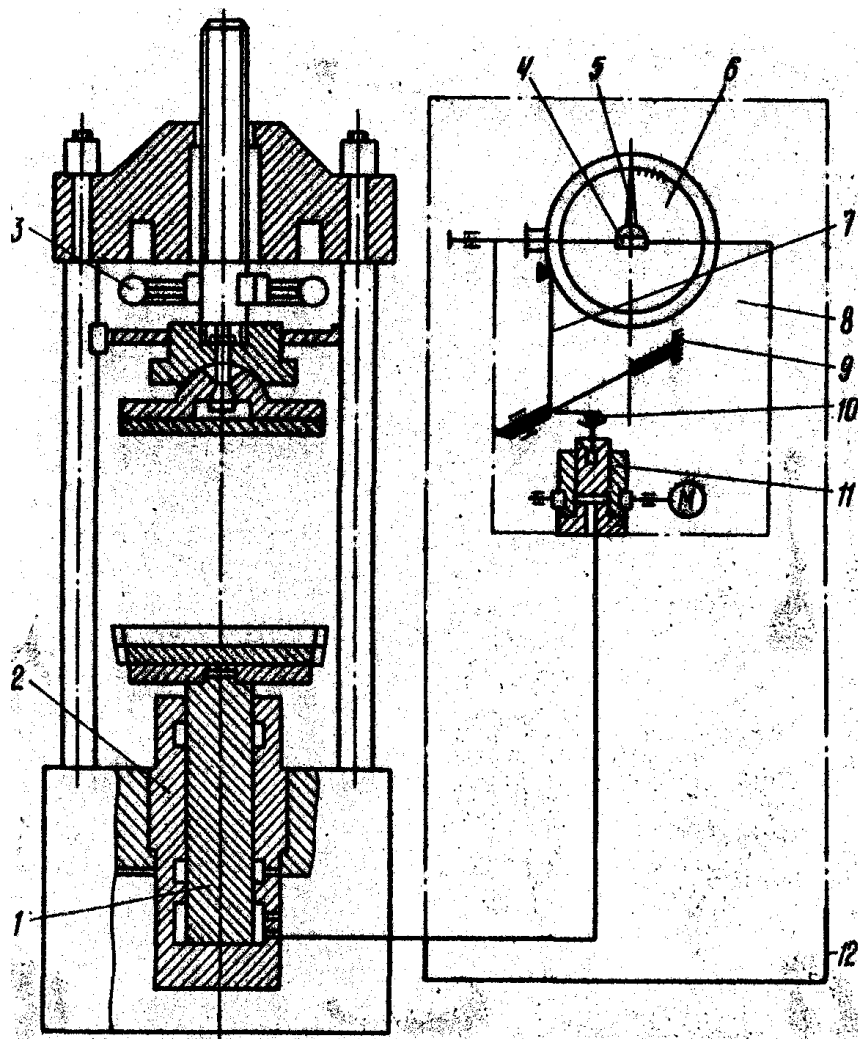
Кінематична схема преса П-10: 1 - плунжер циліндра; 2 - циліндр; 3 - маховик; 4 - рейкова передача; 5 - стрілка; 6- шкала навантажень, 7 – штовхальник; 8 – торсіонний силосвмірювач, 9 - торсіон; 10 – важіль; 11 - силови-мірювач циліндр; 12 – бак для олії
